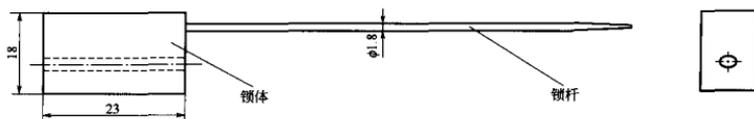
FSG04 罐车锁结构尺寸示意图(单位:mm)
